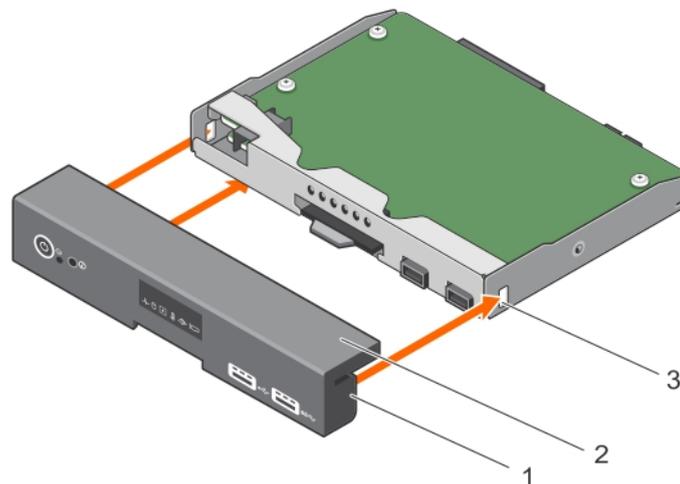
Instalación de la cubierta del ensamblaje del panel de control para un sistema con panel LED.
